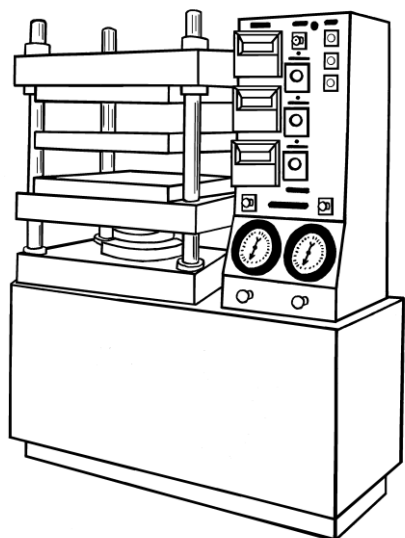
29. Двухъярусный пресс для изготовления МПП
